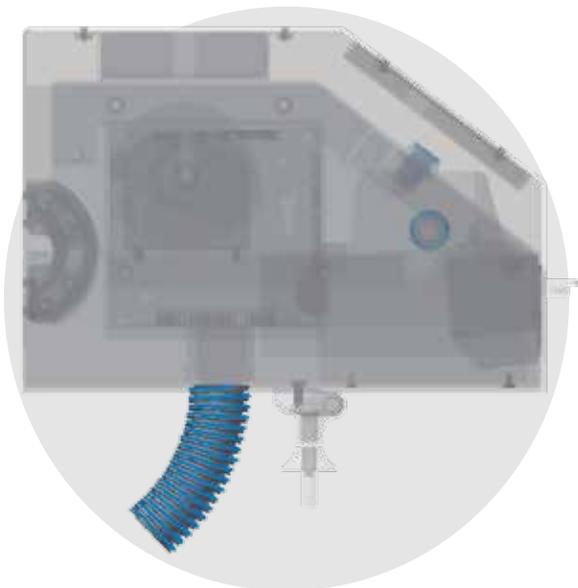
Manguera metálica para proteger los cables. Fuente propia.
